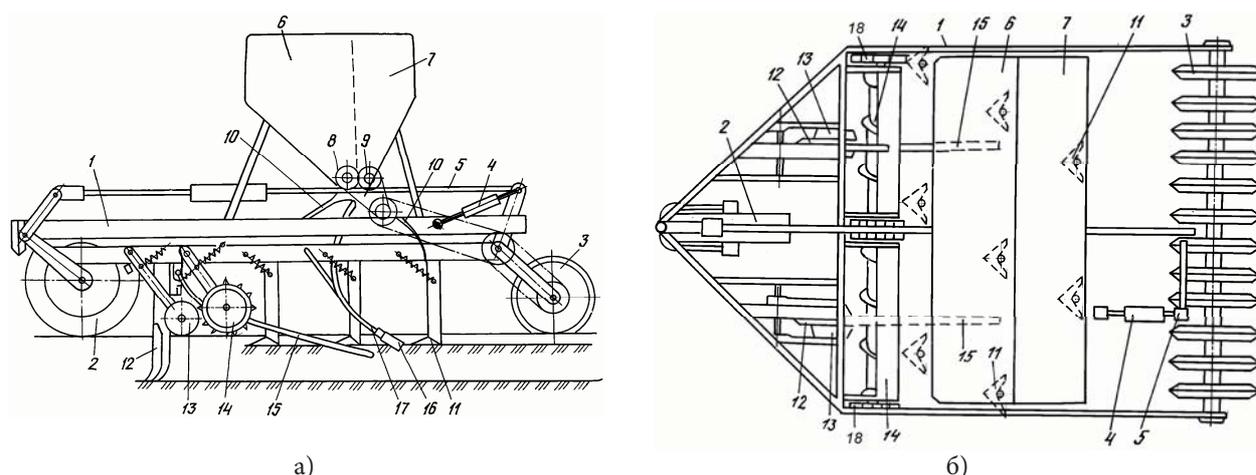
Комплексный почвообрабатывающий агрегат:
